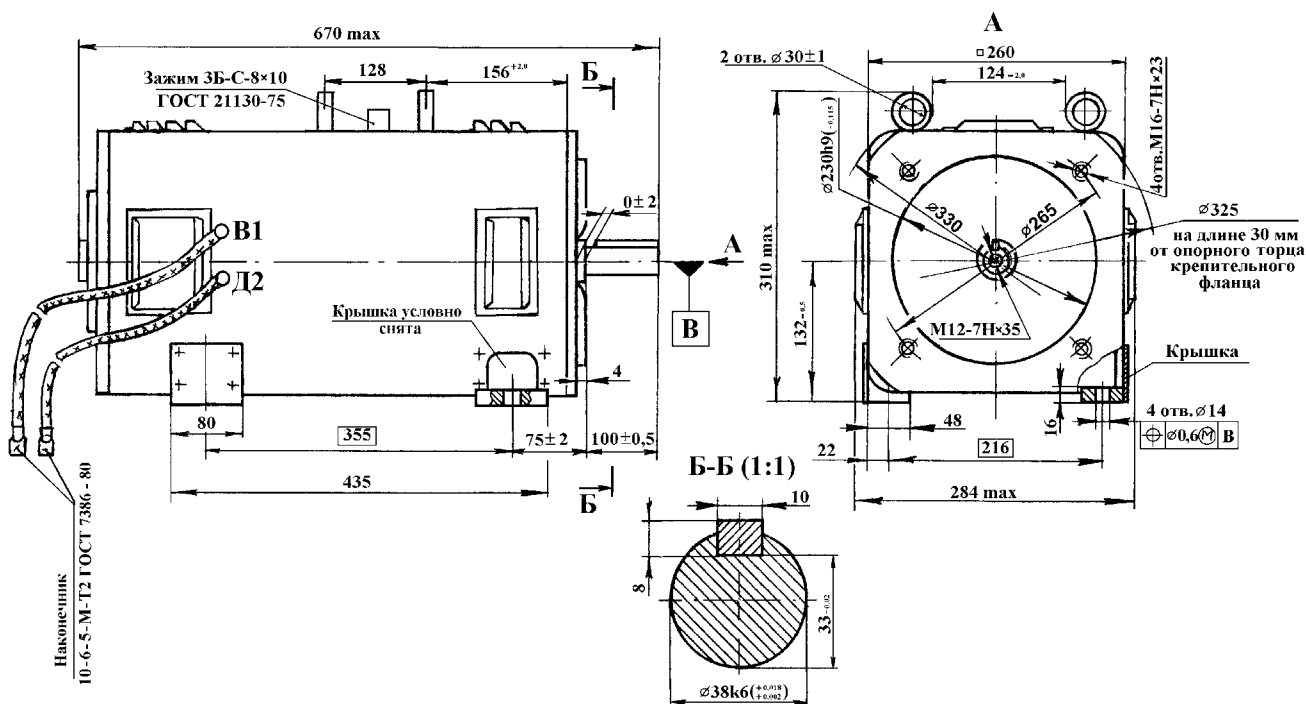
Габаритно-установочные размеры двигателя ПНЖ-132S2-15
